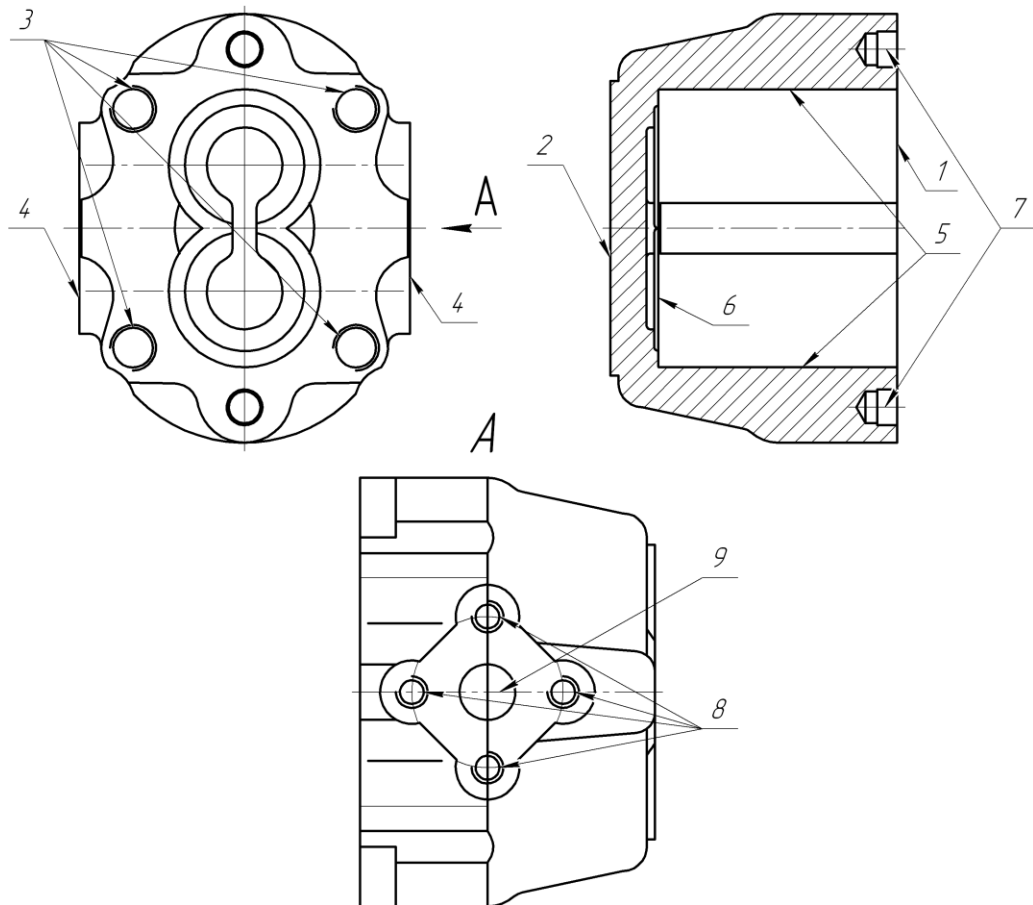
Ескіз деталі корпусу НШ10У-3-02
